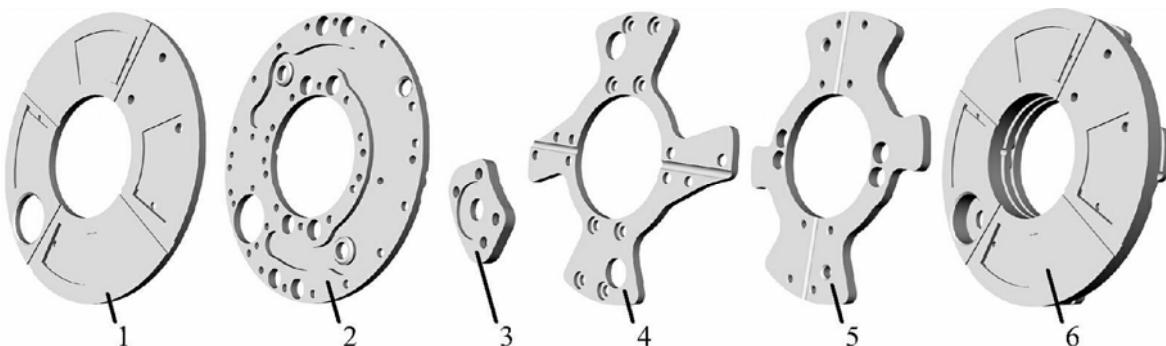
Основные детали и общий вид опытного образца гидростатодинамического подпятника с карманами Рэлея: 1 – верхний диск; 2 – нижний диск; 3 – крышка токовихревого датчика; 4 – верхняя крестовина; 5 – нижняя крестовина; 6 – опытный образец в сборе
